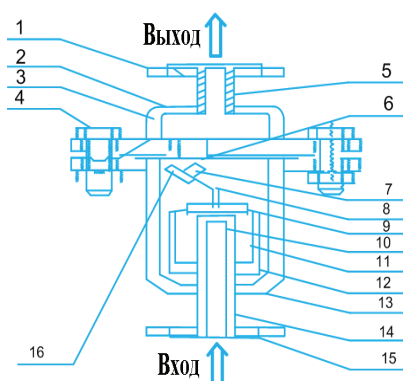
Разрезной чертёж применяемых конденсатоотводчиков, работающих с высоким КПД: 1 — верхний фланец; 2 — пробка; 3 — крышка; 4 — болтовое закрепление; 5 — верхний выходящий трубопровод; 6 — седло; 7 — крутящий клапан; 8 — опора; 9 — закрывающий поплавок; 10 — нижнее отверстие трубопровода; 11 — поплавок; 12 — груз; 13 — корпус; 14 — нижний трубопровод; 15 — нижний фланец; 16 — ось крутящей опоры
